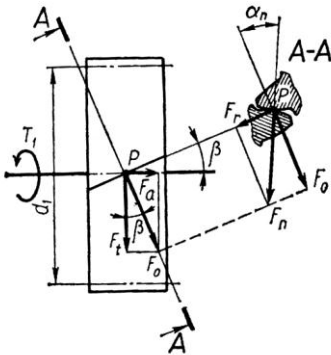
Зусилля на зубці в косозубій циліндричній передачі
